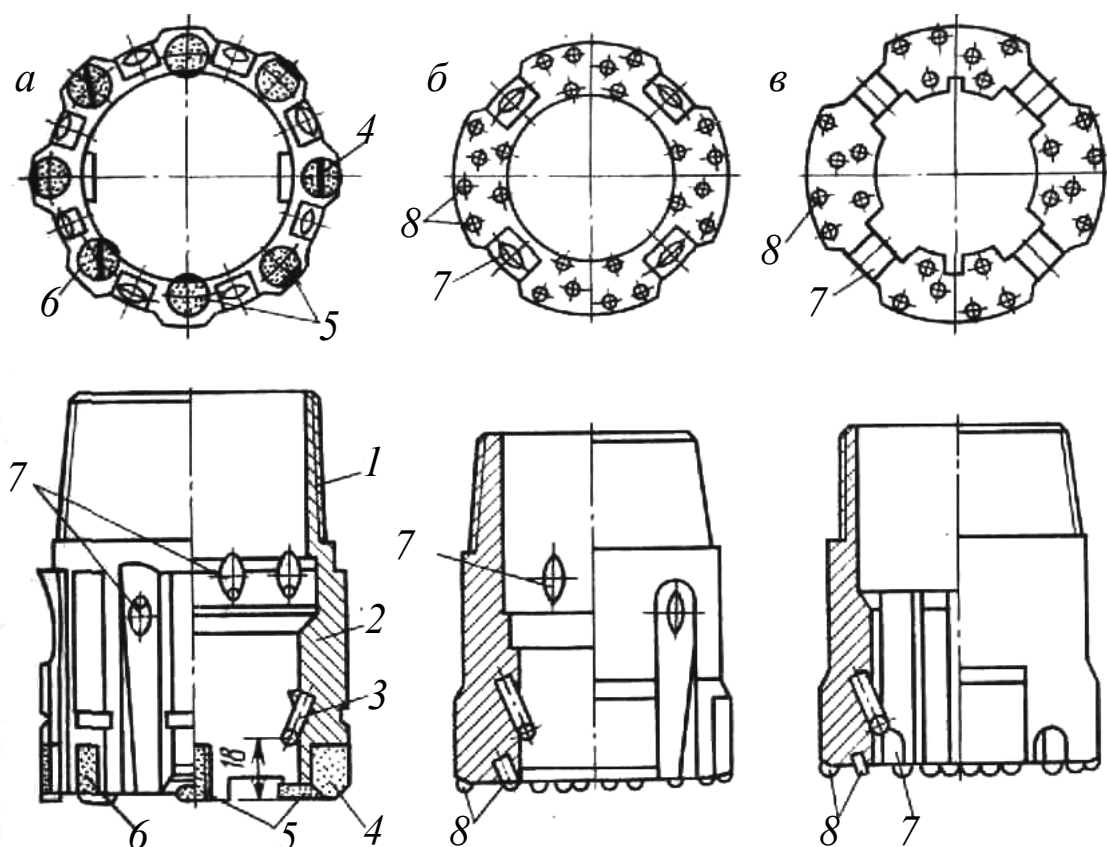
Конструкции долот для ударно-вращательного бурения с пневмоударником: *а* – КДП; *б* – КДП-М; 1 – соединительная резьба; 2 – корончатое кольцо; 3 – скоба кернорвателя; 4, 5, 6, 8 – твердосплавные вставки различной формы; 7 – циркуляционные окна
